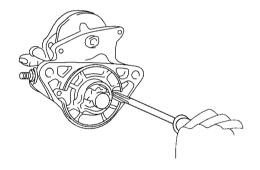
拆下起动机外壳、中间齿轮、轴承和离合器部件
